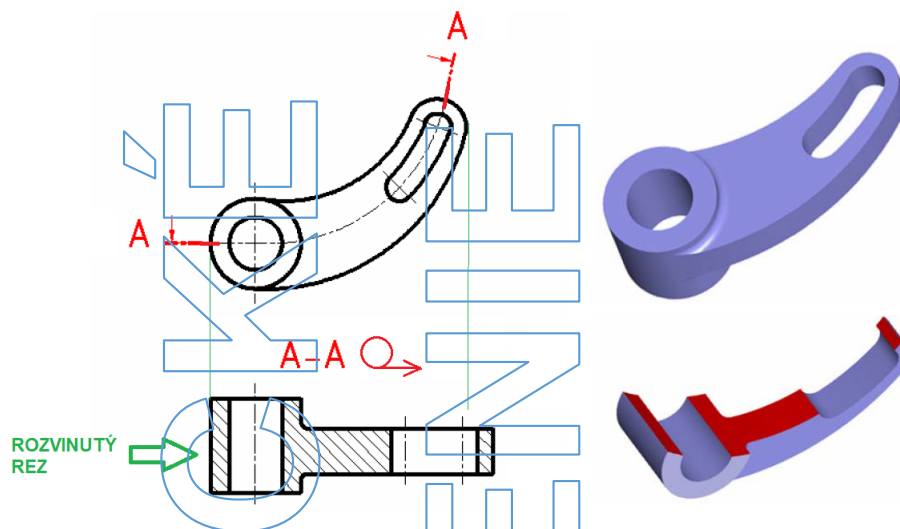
Príklad správneho zobrazenia súčiastky
